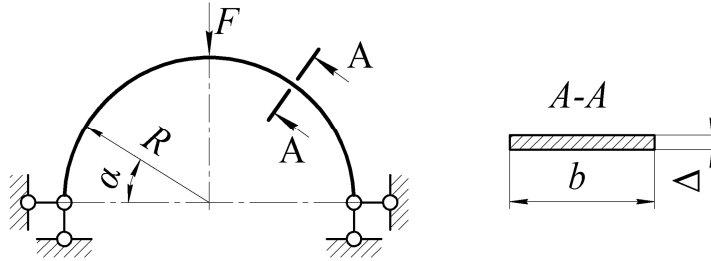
Розрахункова схема виступу зіркоподібної пружини
